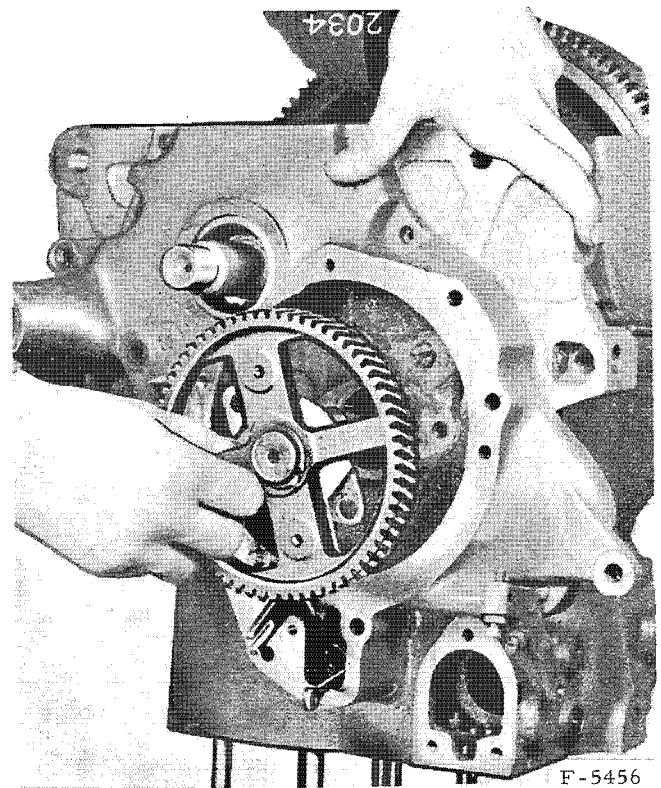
Démontage de l'arbre à cames pour remplacer la plaque poussée.
